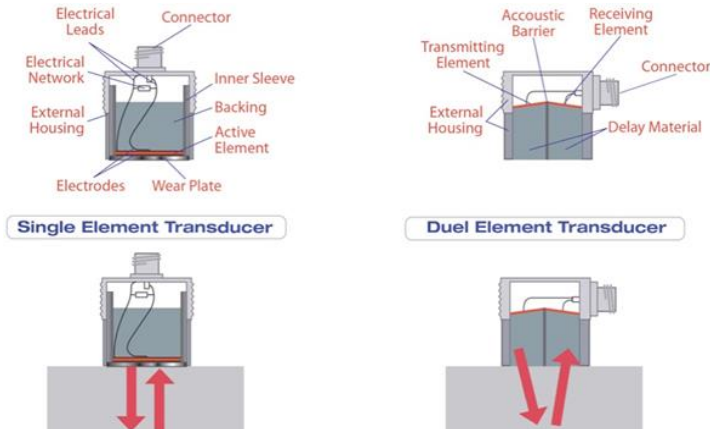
Ilustrasi Komponen Pada Sebuah Piezoelectric Transducers (Probe). Tipe single element (Tecs, 2024)
